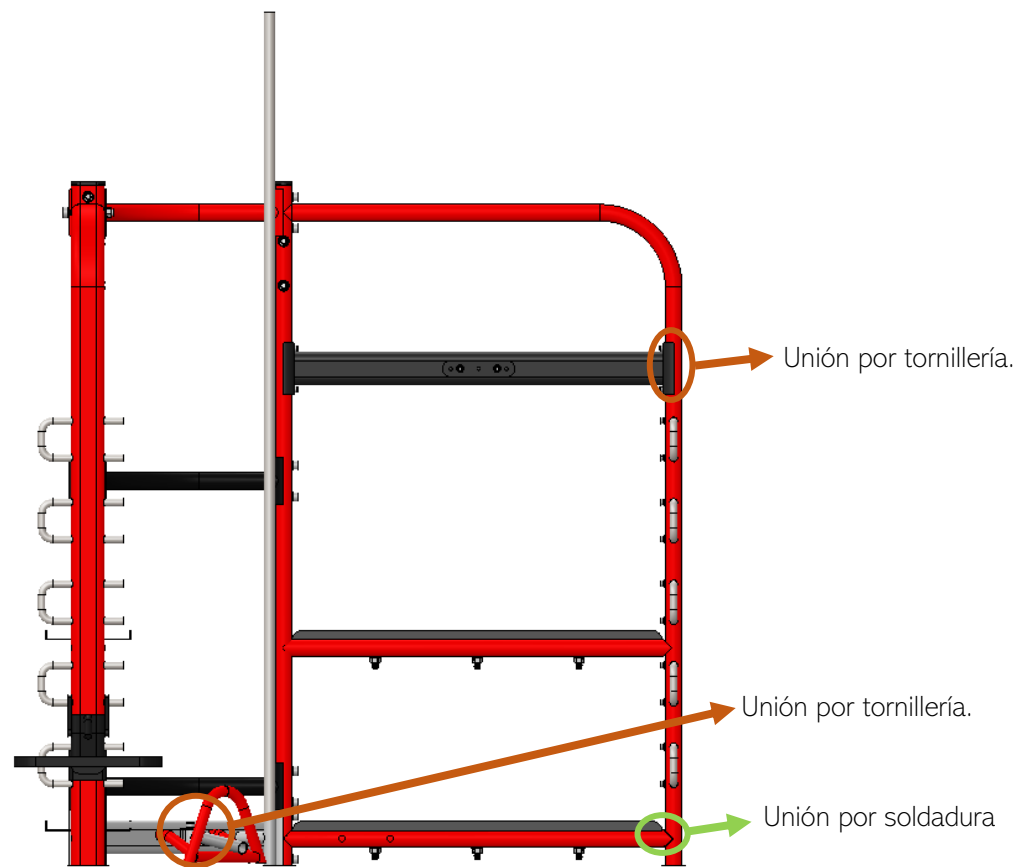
Soldadura y uniones del subconjunto 3. Fuente: Elaboración propia
